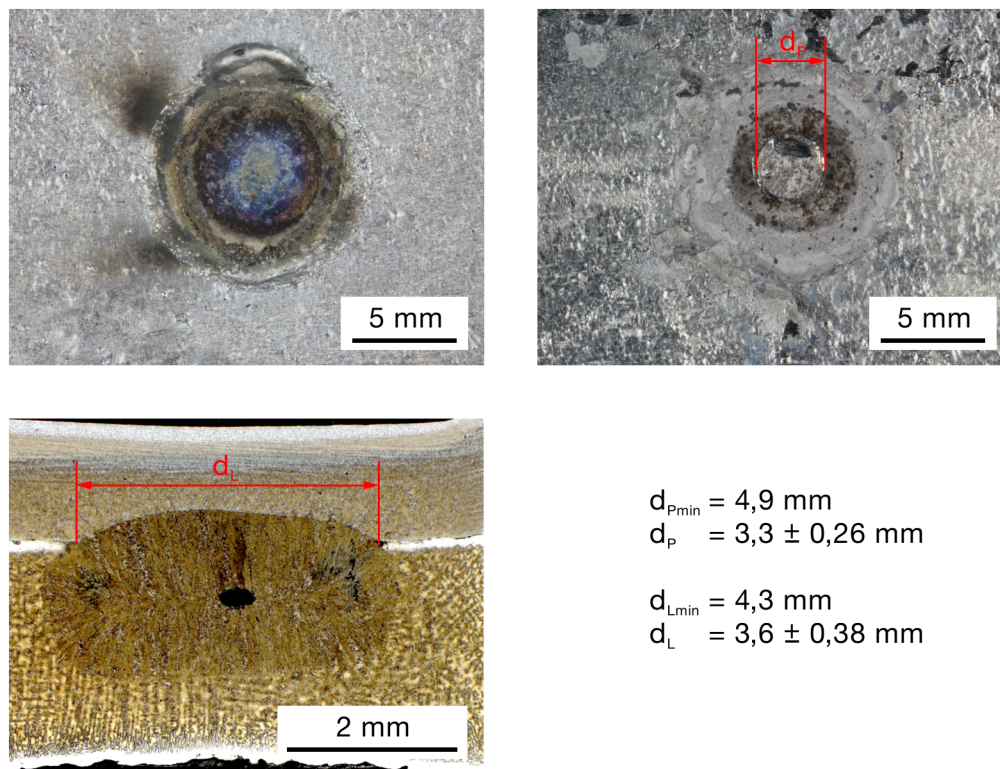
Schweißpunkt auf einer feuerverzinkten Stahlgussprobe (oben links) nach dem Ausknöpfen (oben rechts) und Schliffbild einer Schweißlinse (unten links)
